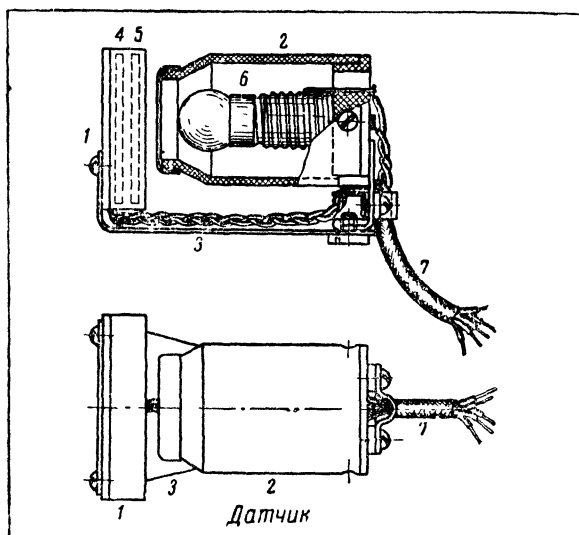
Датчик: 1 — корпус фотоэлемента; 2 — корпус осветителя; 3 — плоская пружина; 4 — дифференциальный фотоэлемент; 5 — светофильтры; 6 — лампа; 7 — многожильный шнур
